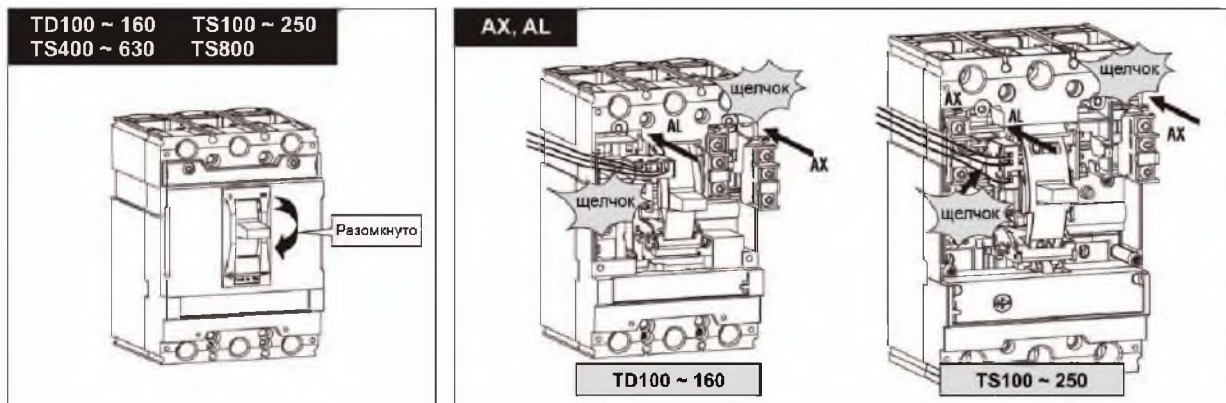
Установка блок-контактов AX, AL в выключатели TD100-TD160, TS100-TS250
